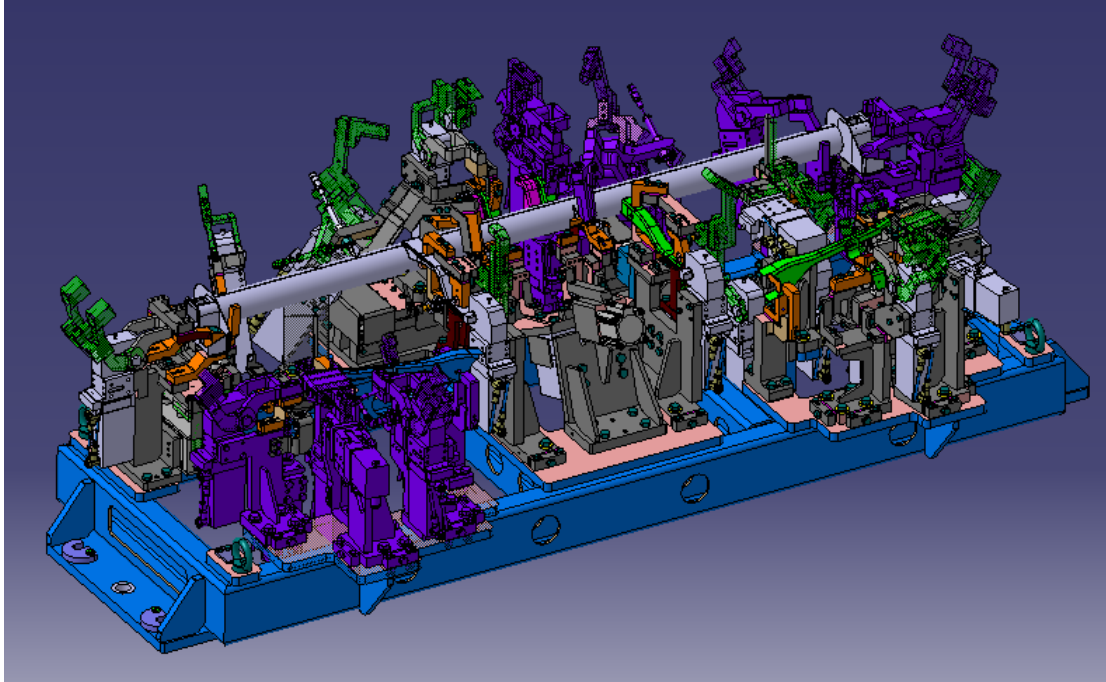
Diseño del utillaje de soldadura. Fuente: Interob (2016).
